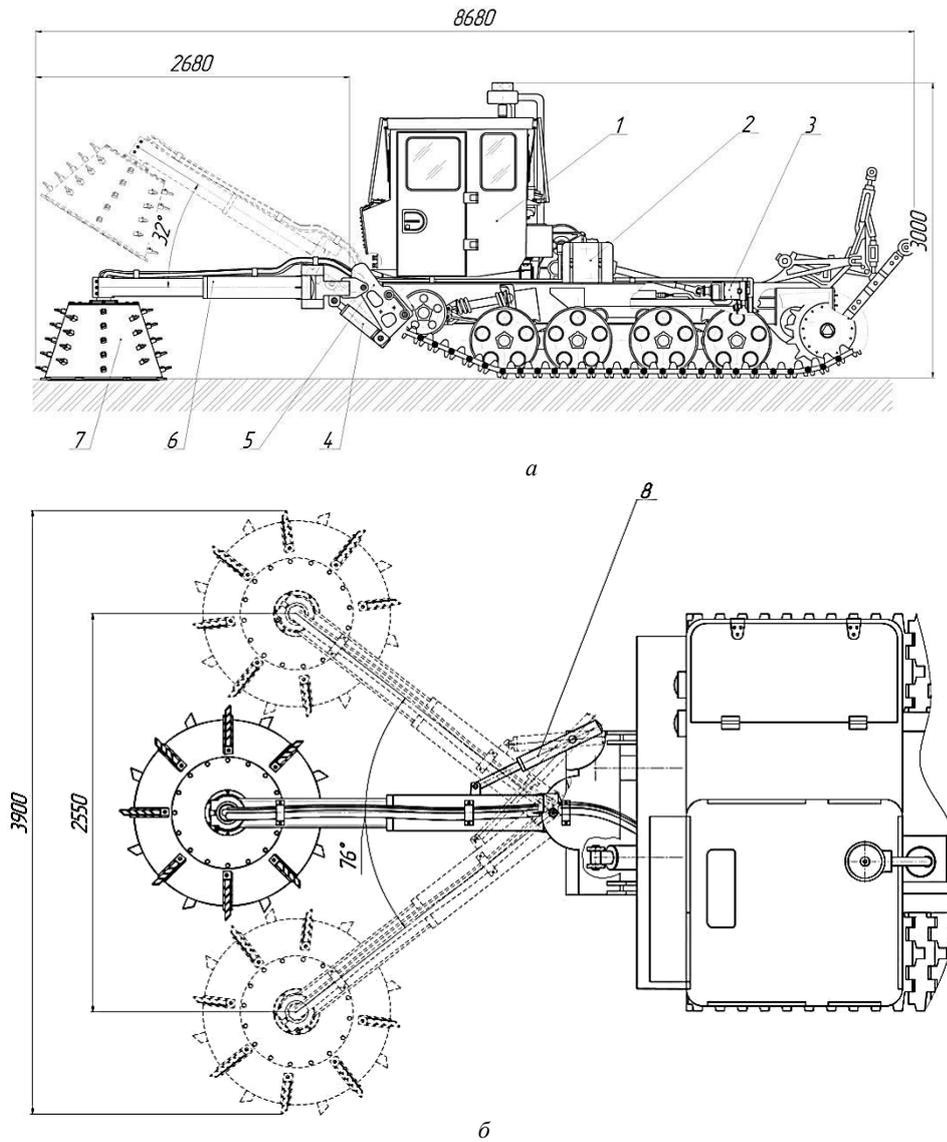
Общий вид проектного орудия: *а* – вид сбоку, *б* – вид сверху; 1 – базовый трактор; 2 – бак масляный; 3 – гидронасос; 4, 8 – гидроцилиндры; 5 – навеска; 6 – стрела; 7 – фреза
